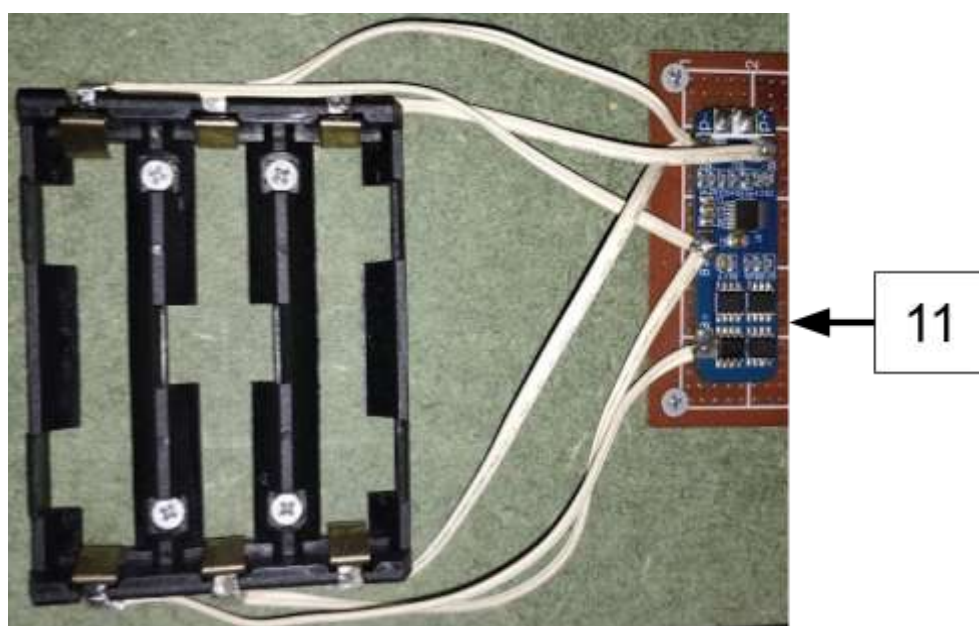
Placa De Proteção Bms 3s 20a 12.6v + Suporte para 3 baterias 18650 Soldado
